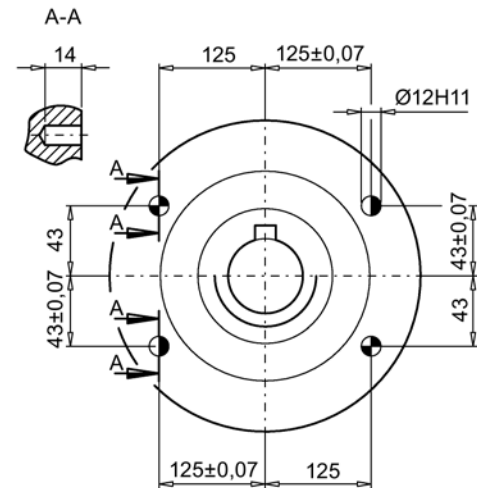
C-Typ Gehäuseflansch Stirnradgetriebe
